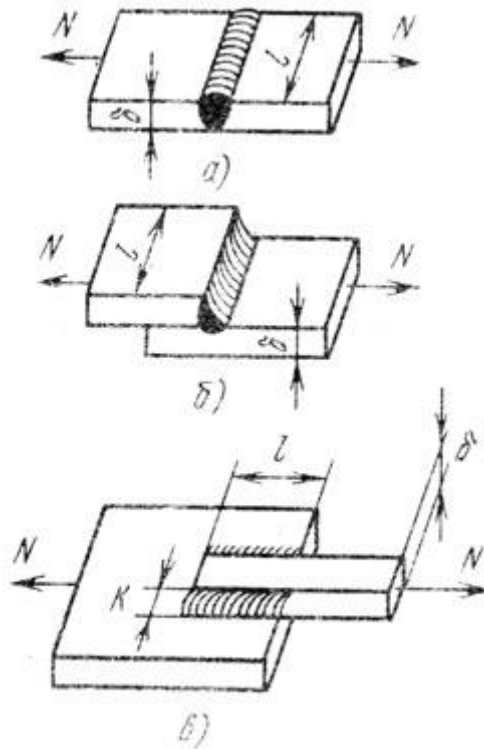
Нагрузки на сварные швы: а - стыковой, б - угловой лобовой, в - угловой фланговый
